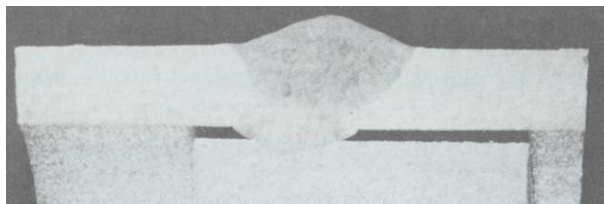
焊接背板支承不当引起的管焊缝根部缺陷
